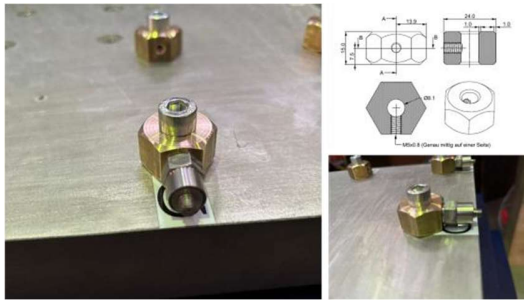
Mithilfe eines Messingadapters in x-Richtung positionierter KS78C.100 Beschleunigungssensor von vorne (links) und von der Seite (rechts unten) sowie eine technische Zeichnung des Messingadapters (rechts oben)
